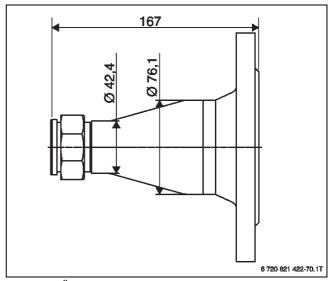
Übergangsstück DN 65/PN 16 – G 1 ½ " (Maße in mm)
